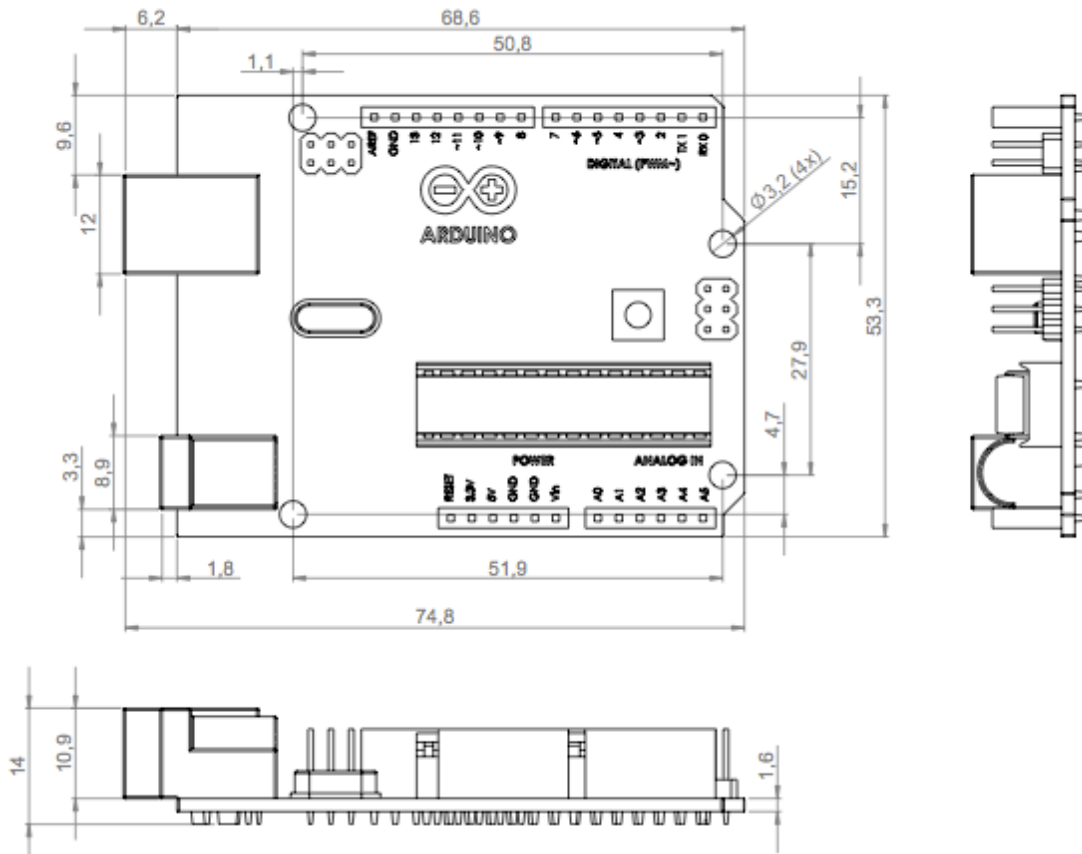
Vistas con dimensiones en alzado, planta y perfil de Arduino UNO
